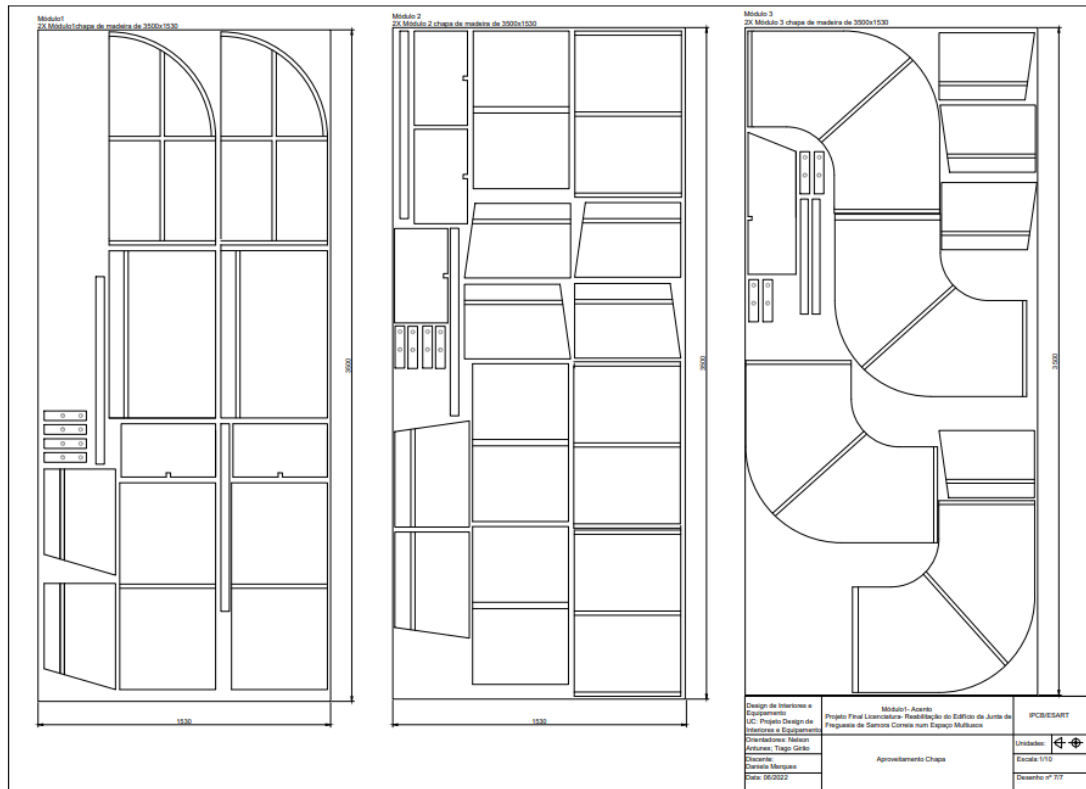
Figura 102-Desenho Técnico Aproveitamento Chapa
